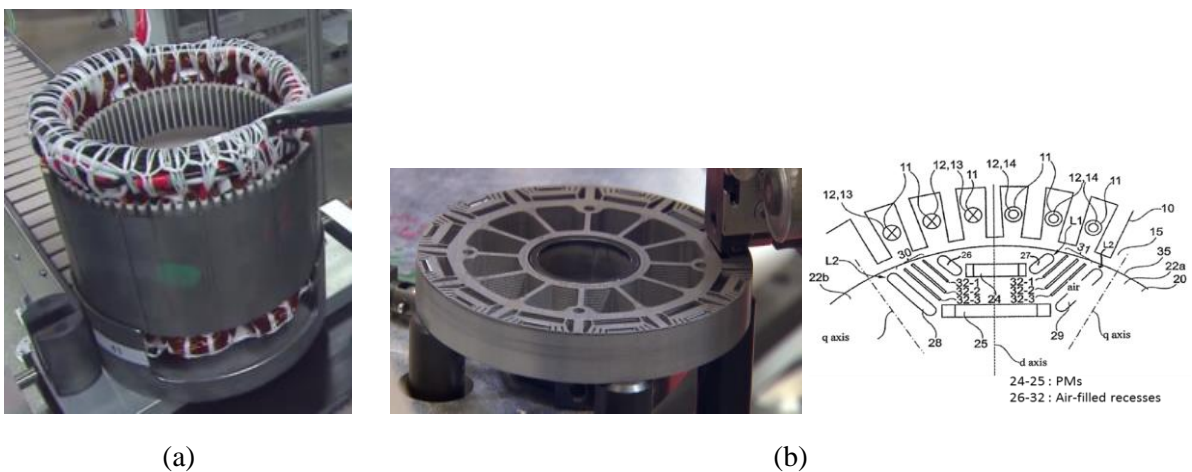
BMW i3 : (a) stator à bobinage distribué et (b) rotor à APs enterrés [27]-[28].
